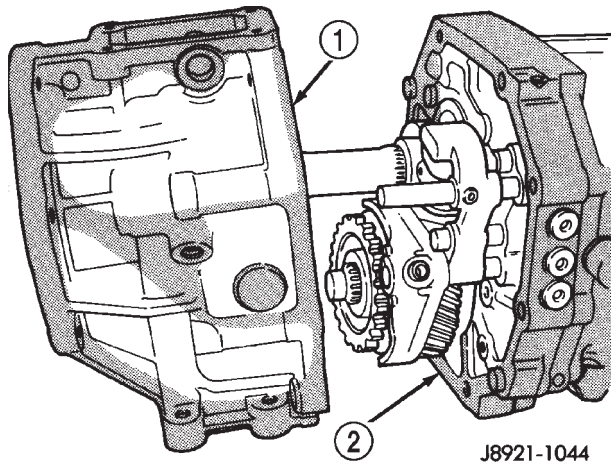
Desmontaje de cubierta del adaptador o retenedor de cojinete trasero - Característica
